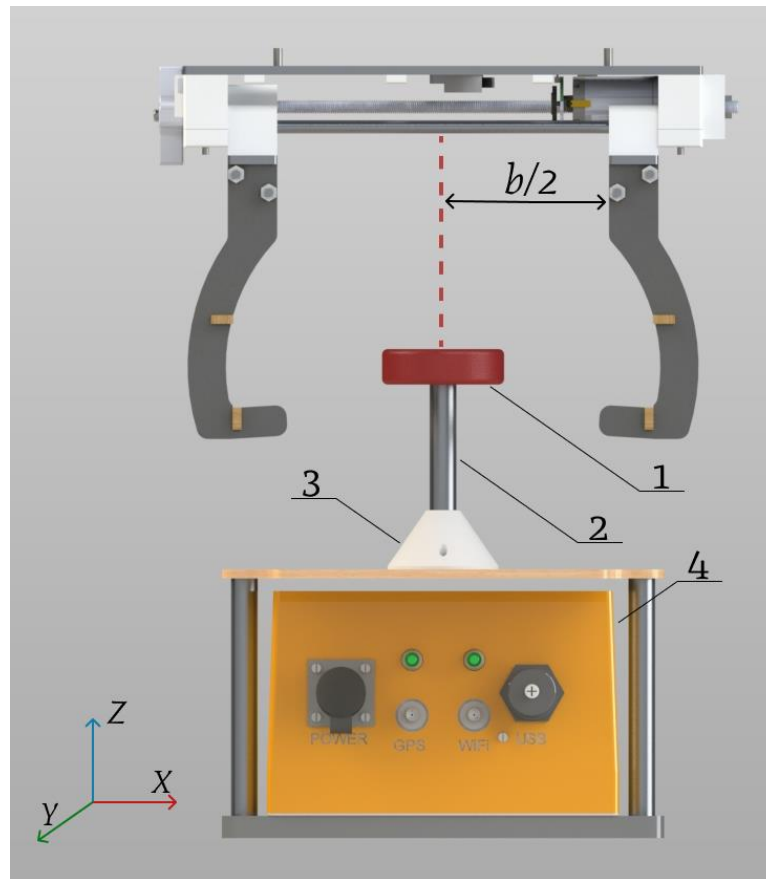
Транспортное крепление датчика сейсмической активности и захват
